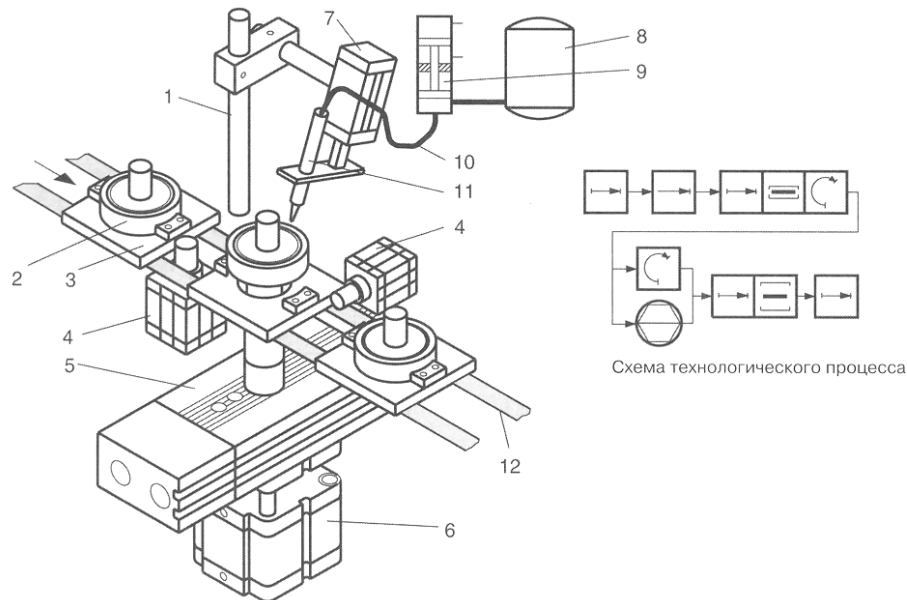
Устройство для нанесения клея: 1 – штатив; 2 – подлежащий склеиванию узел; 3 – держатель заготовок; 4 – стопорный цилиндр; 5 – поворотный модуль; 6 – подъемный цилиндр; 7 – пневматический цилиндр; 8 – бачок с клеем; 9 – дозирующий насос; 10 – трубопровод для подачи клея; 12 – транспортер.
